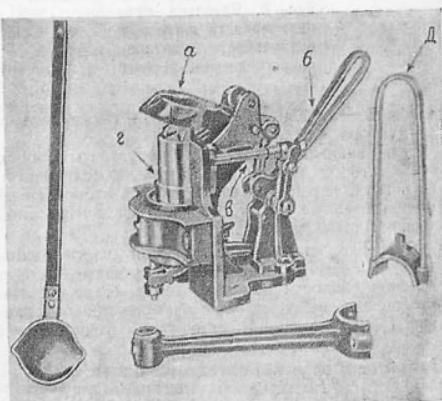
Прибор для заливки шатунных подшипников и крышек коренных подшипников
